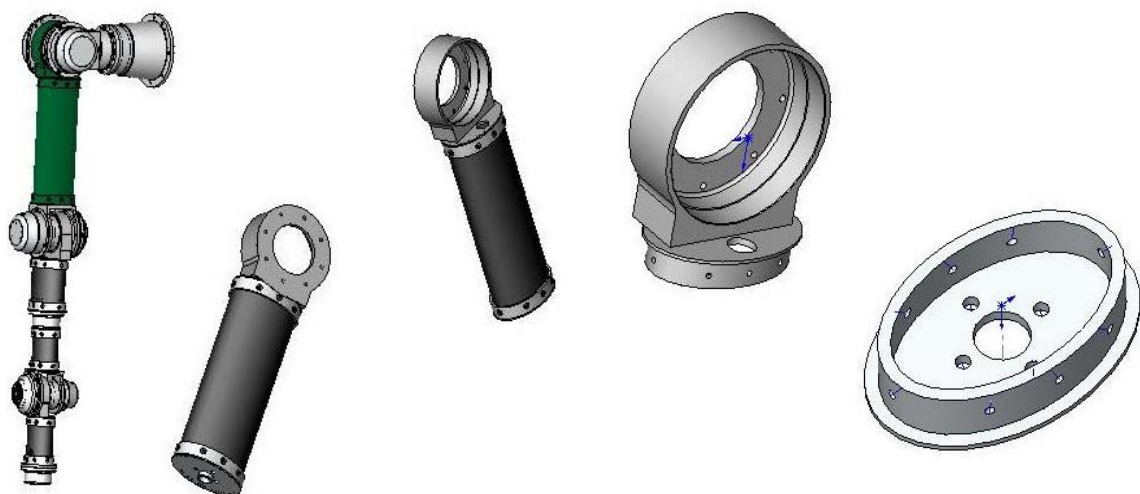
Vista sub-ensamblaje sección elíptica y piezas de la misma sección.
